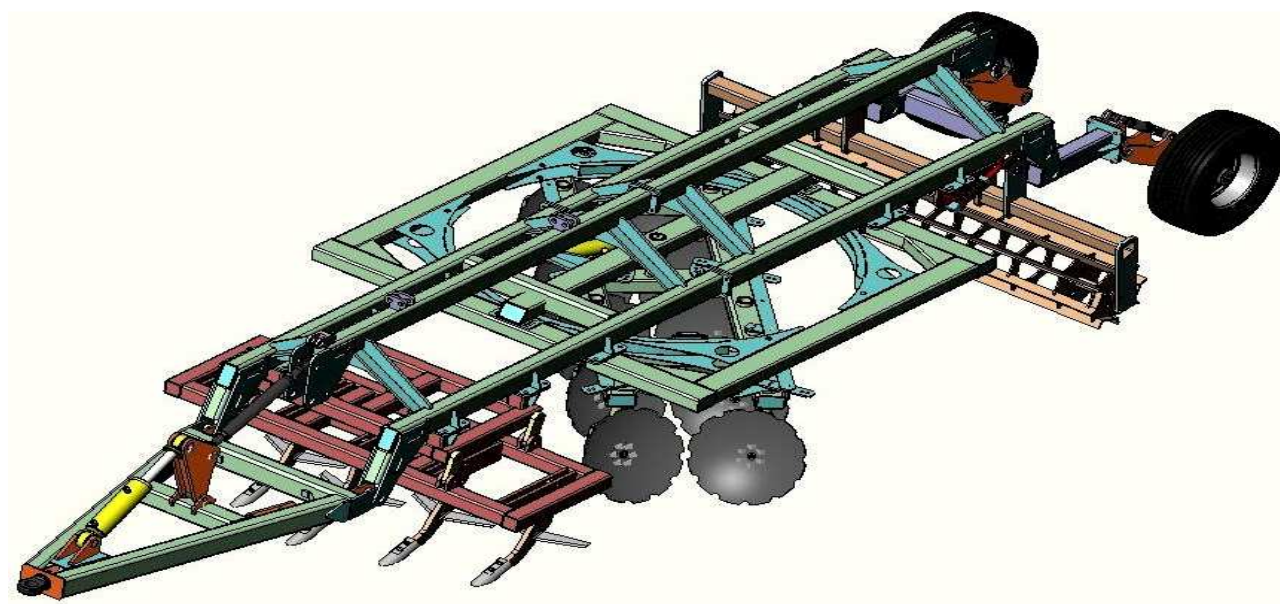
Агрегат почвообрабатывающий универсальный АПУ-1 в сборе – отладка (режим вспашки)
